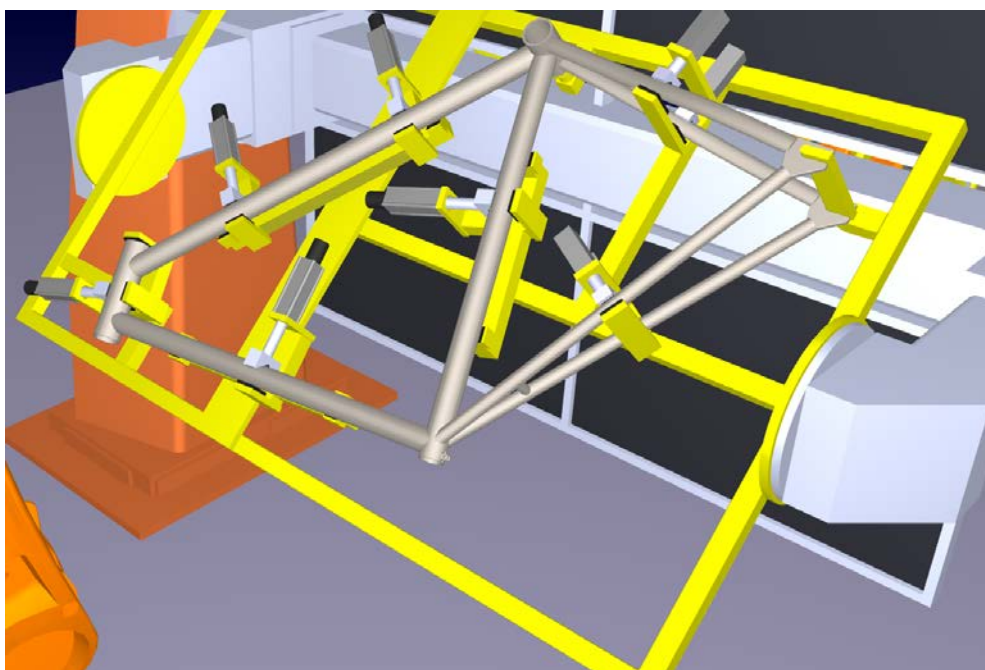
Загальний вигляд рами, зафіксованої на одноосьовому механізмі обертання KUKA KP1 H250 EN980 для зварювання рами
